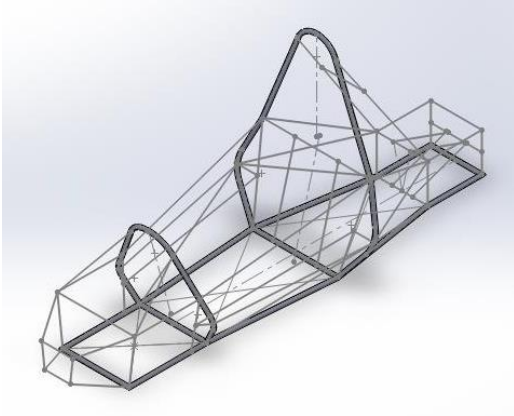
Modelado 3D de las estructuras del chasis con perfil tubular.
